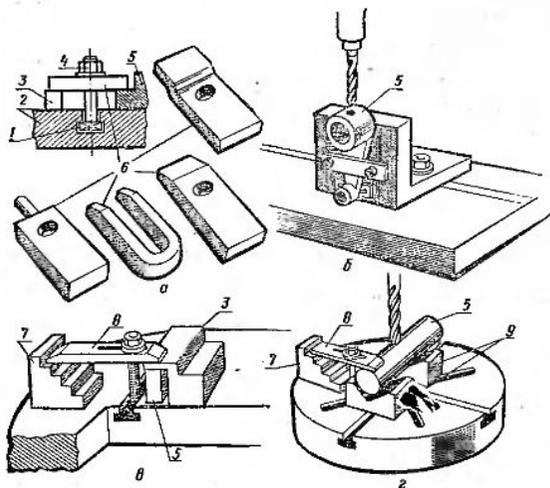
Приспособления для установки обрабатываемых изделий на столе сверлильного станка:
